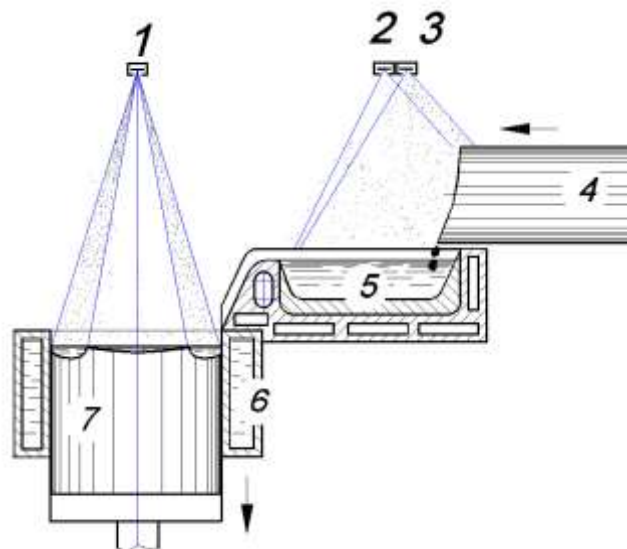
Схема ЕПП з проміжною ємністю: 1-3 - електронно-променеві гармати; 4 - витратна заготовка; 5 - проміжна ємність; 6 - кристалізатор; 7 - зливочна форма
